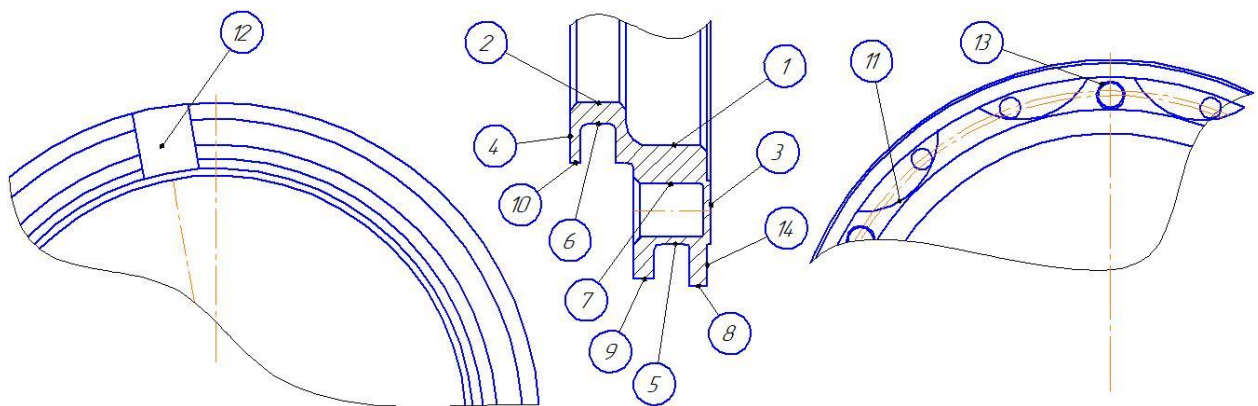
Технологічна розмітка поверхонь деталі «Поршень»
